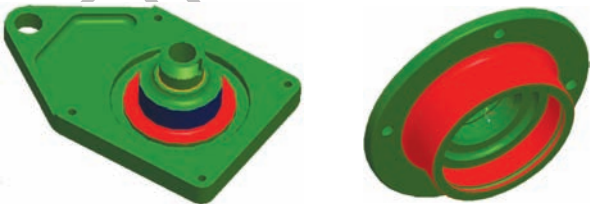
轴承座上的轴承安装座 图 11 轴端法兰盘上的轴承室
